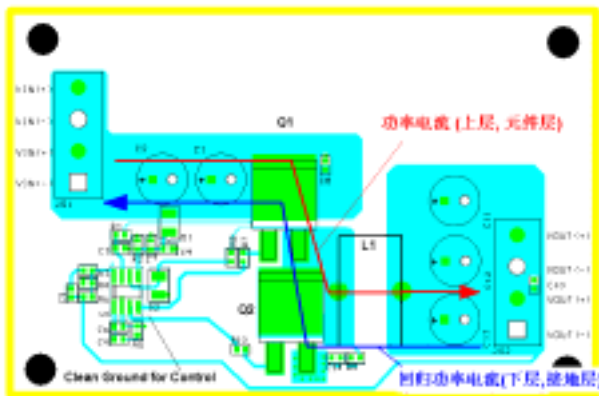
降压式开关电源 PCB 上层图 (下层是接地层)
